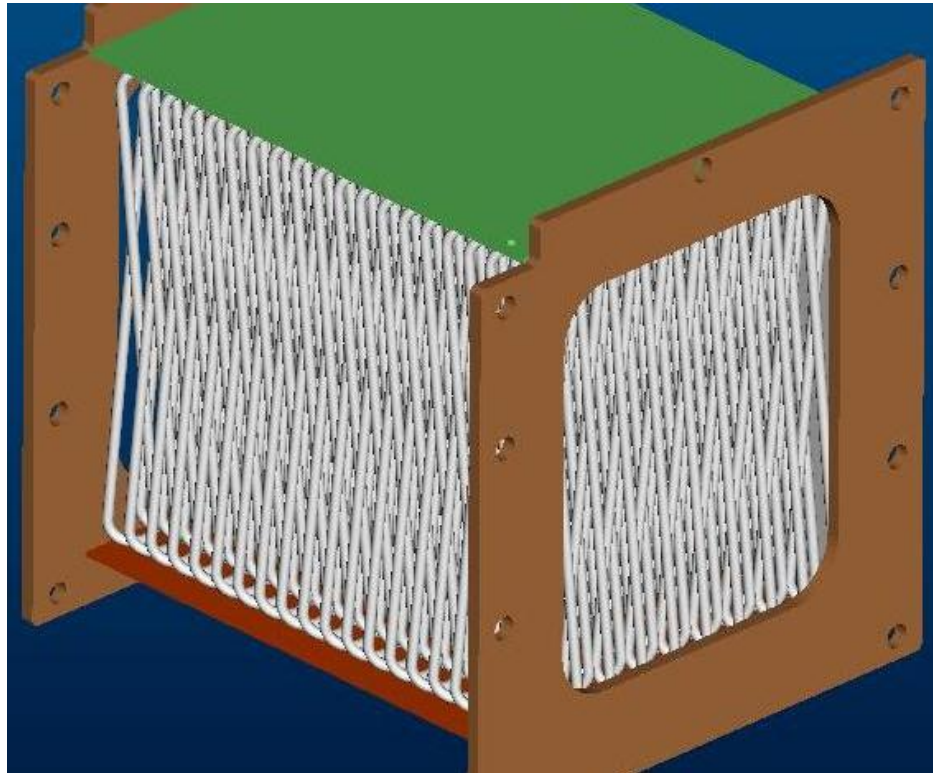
Prinzipskizze eines Rohrbündeldampferzeugers 02
